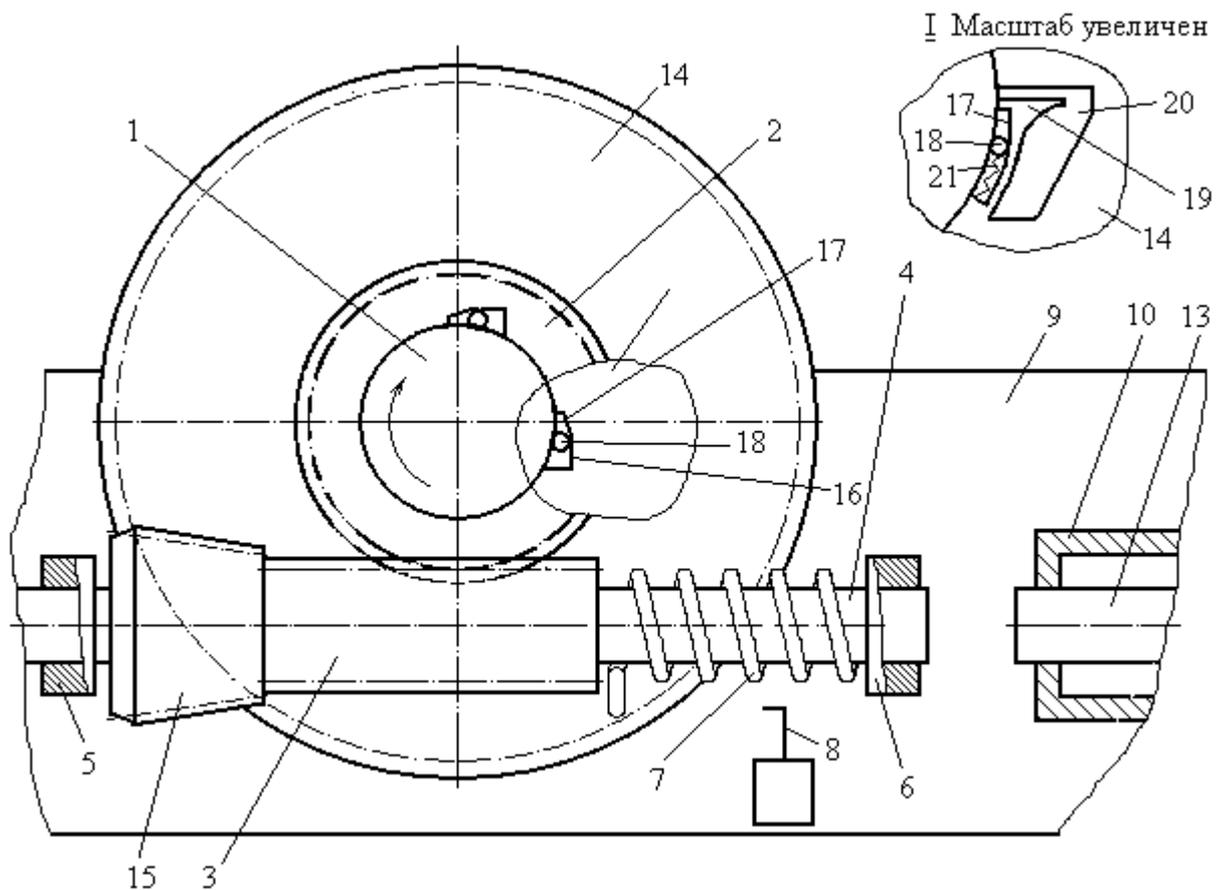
Гайковерт с двумя зубчатыми передачами
